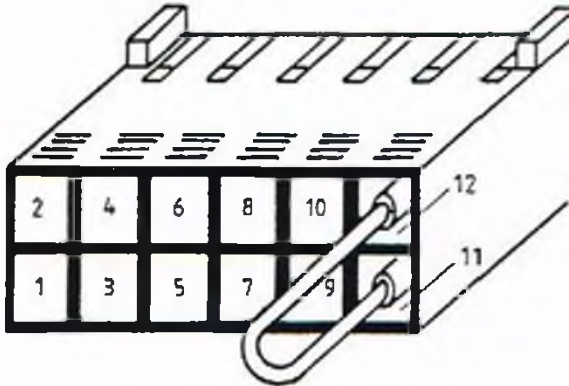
Endstecker (siehe auch Kap. 2.3)
